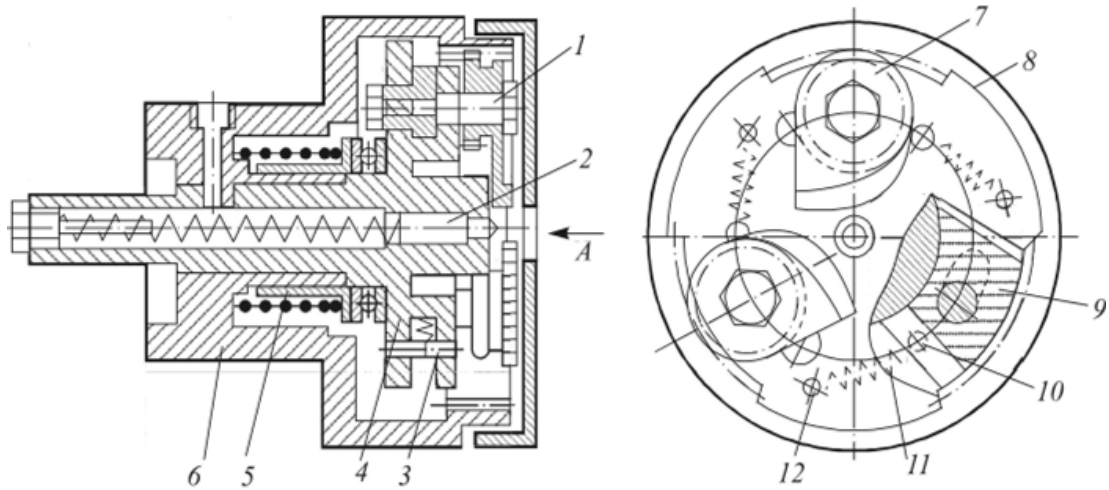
Повідковий самозатискний трикулачковий патрон
